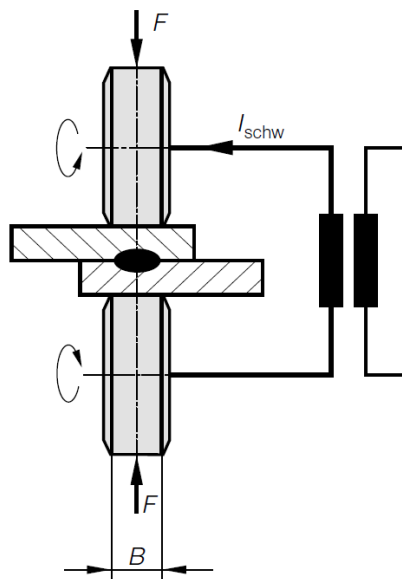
Verfahrensprinzip Rollennahtschweißen [5]
